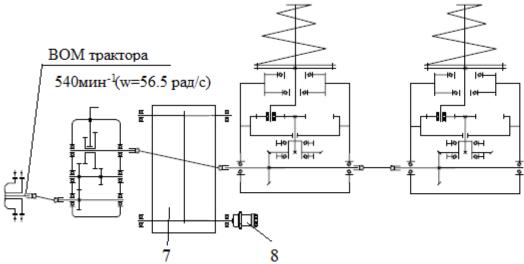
Схема кинематическая (трансмиссии) кормораздатчика СРКВ-15 (СРКВ-13, СРКВ-17) с реверсивным транспортером.
